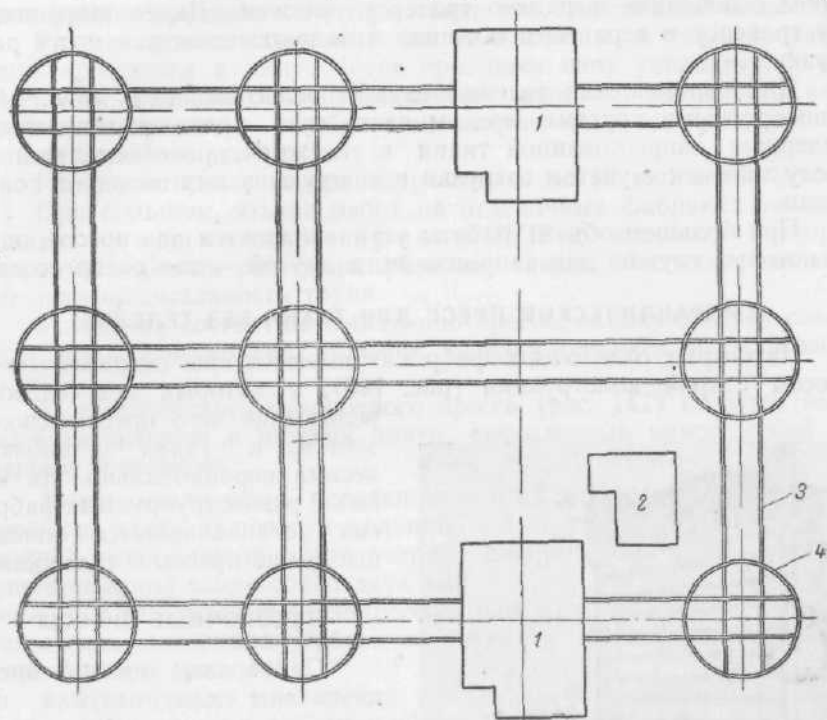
Схема рельсовых путей для двух прессов Б-301:
